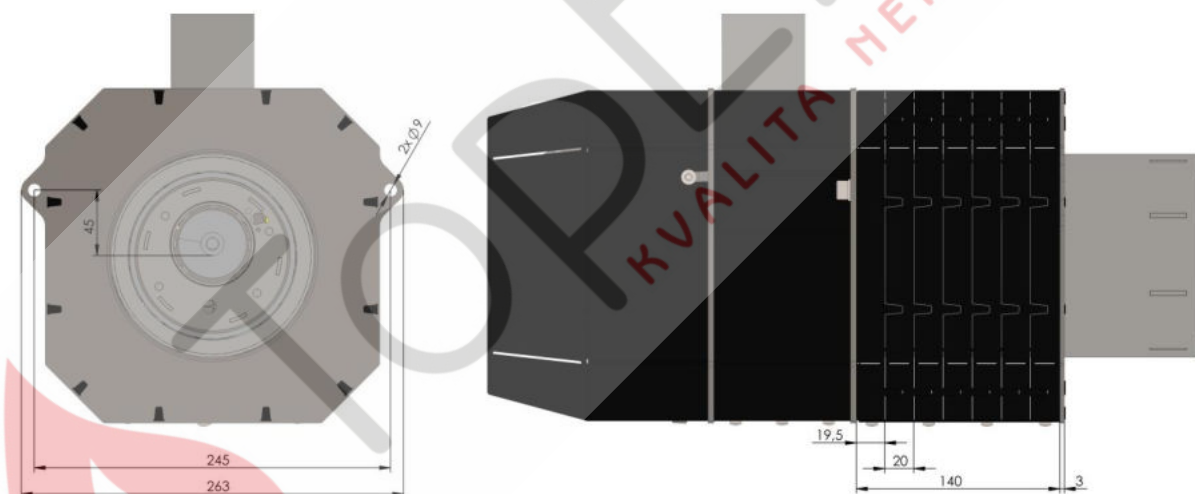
Pohled na hořák 6-26 kW s izolačním pláštěm a montážní deskou.
